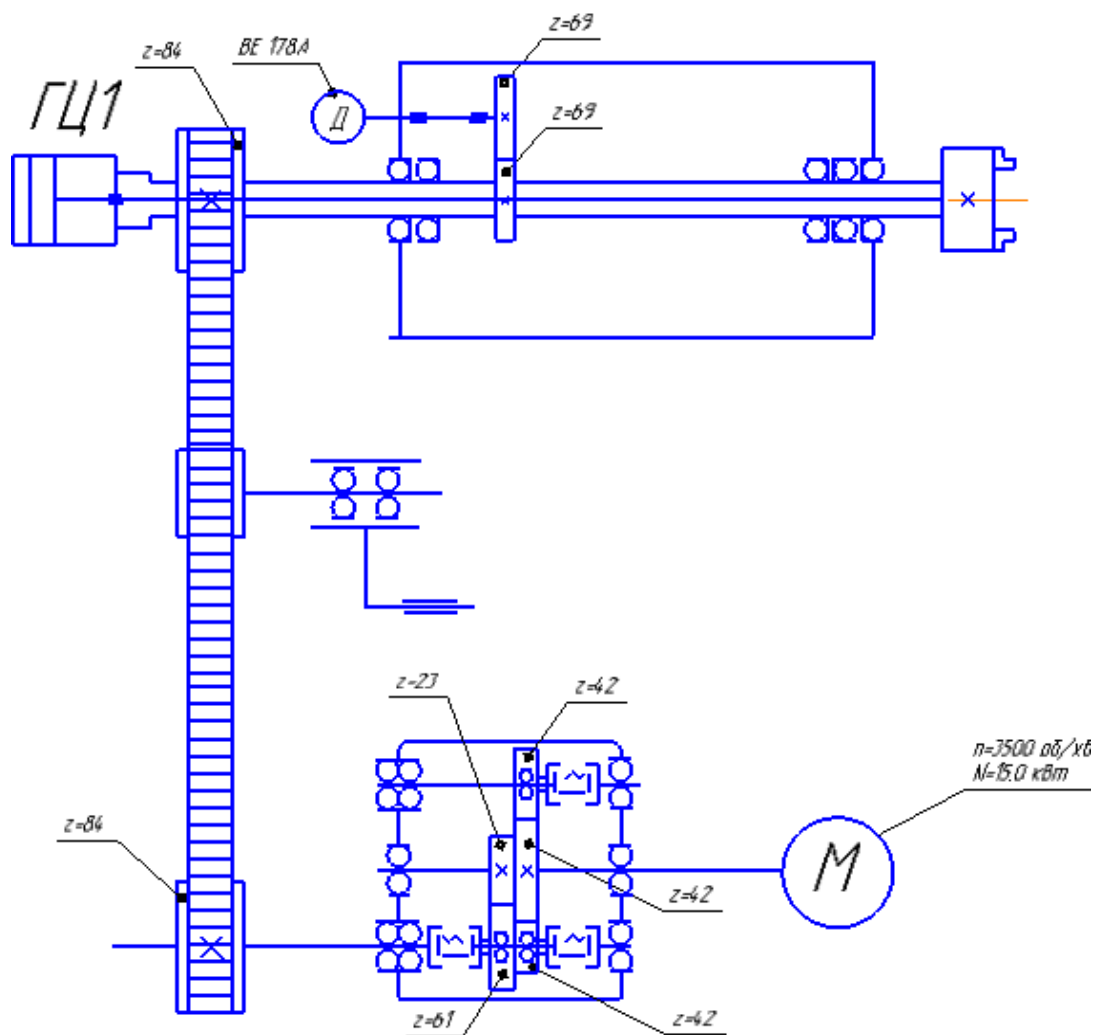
Кінематична схема приводу головного руху токарного верстата з ЧПК
